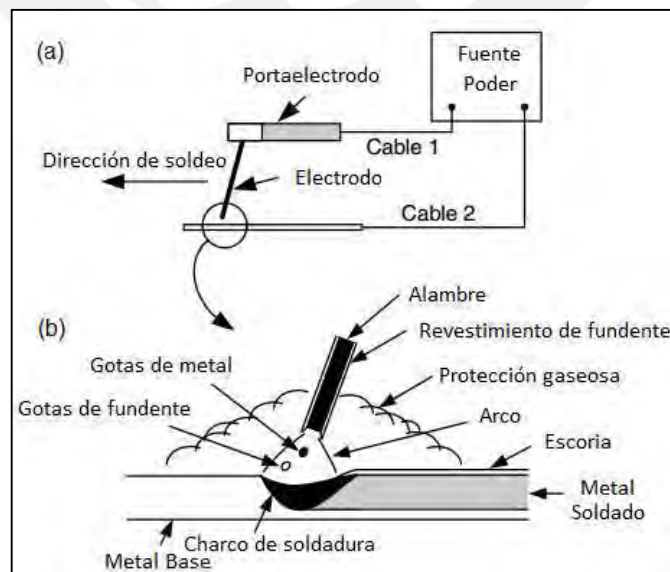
Proceso SMAW: (a) proceso general; (b) área de soldadura ampliada [11].
